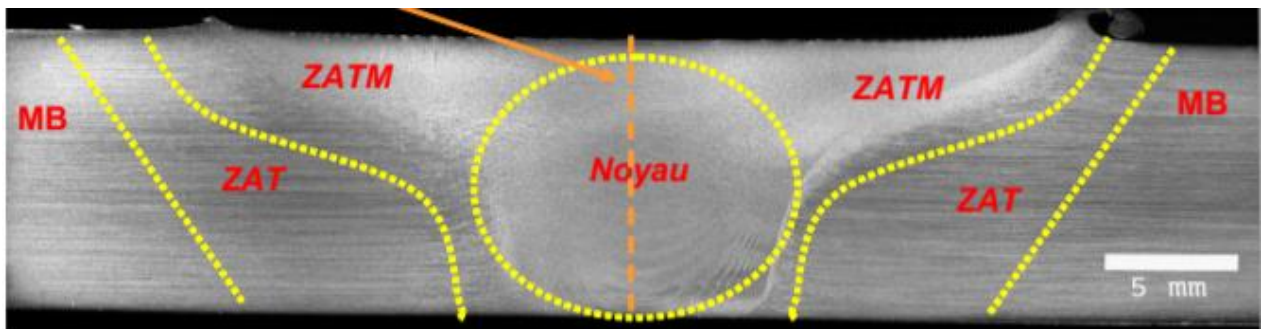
Macrographie d'une soudure FSW d'un alliage d'aluminium
